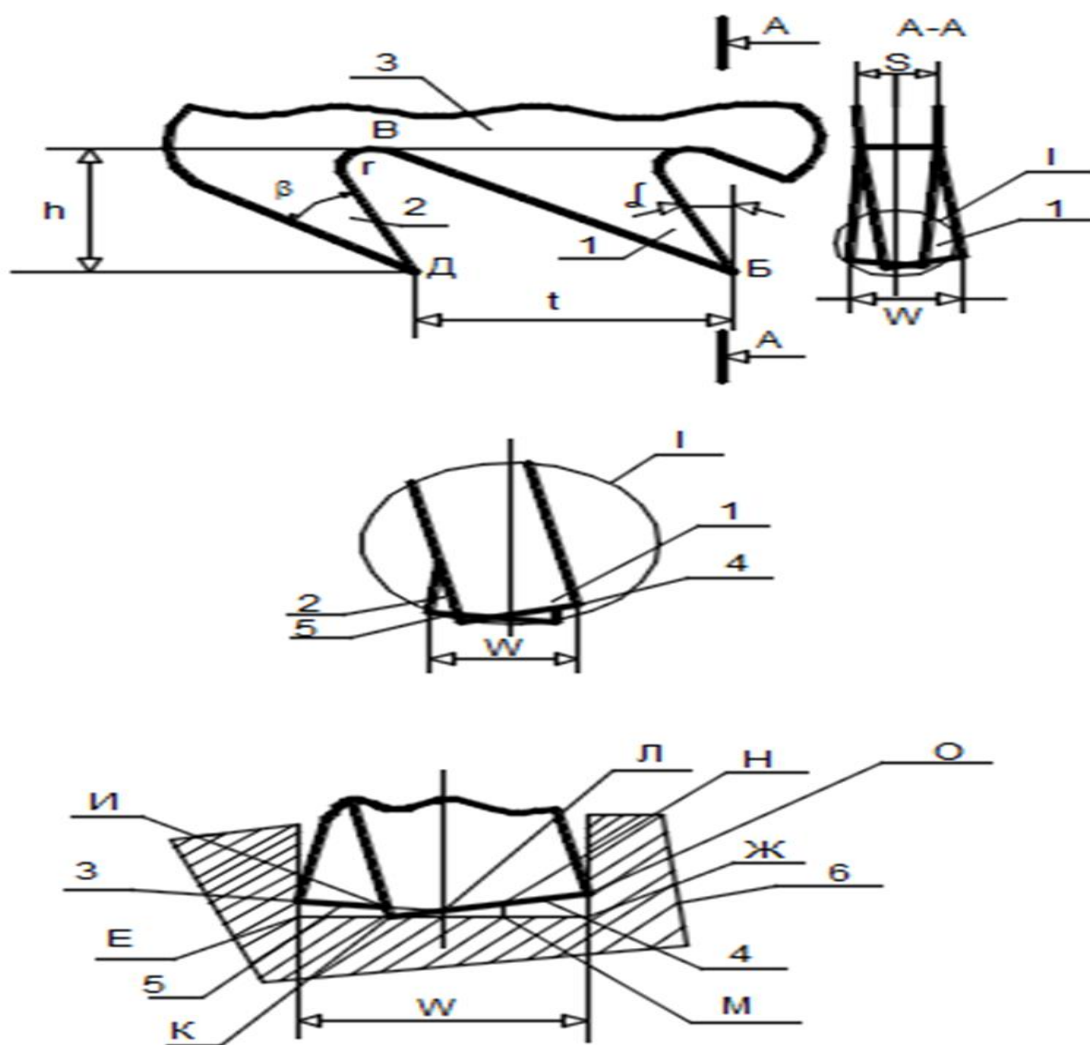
Схематичное представление конструкции пилы с зубьями для вывода стружки из пропила [2]
